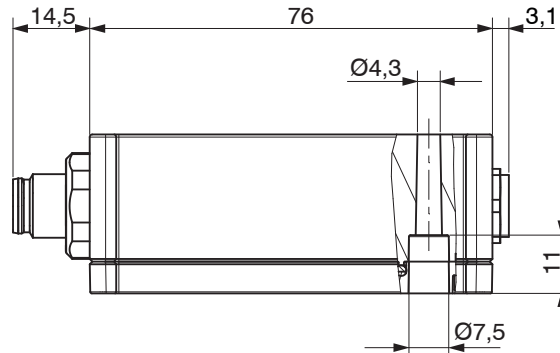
Maßzeichnung des Controllers MSC7401(010), Abmessungen in mm
